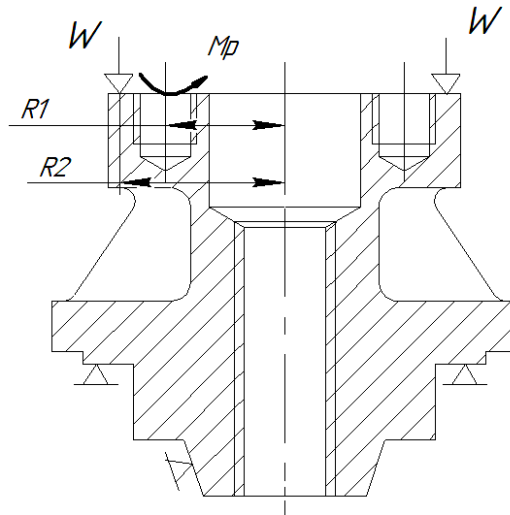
Схема базування та закріплення заготовки на операції свердлування
